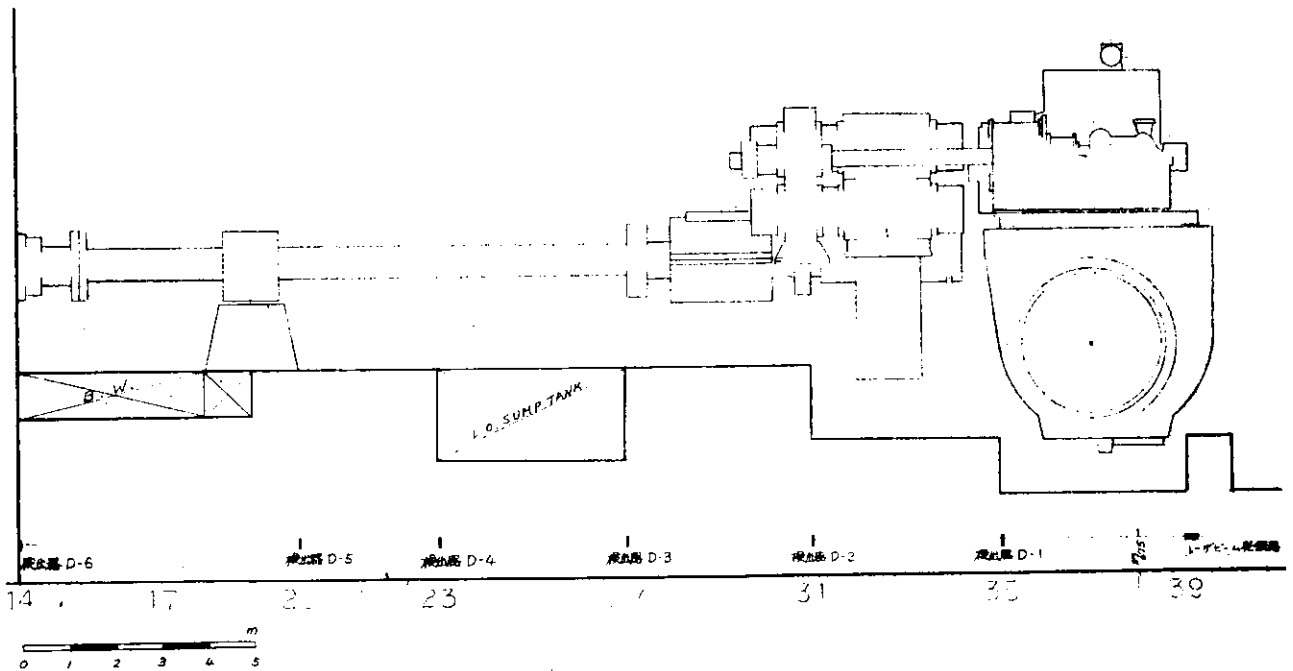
機関室二重底計測位置 (ELEVATION)
